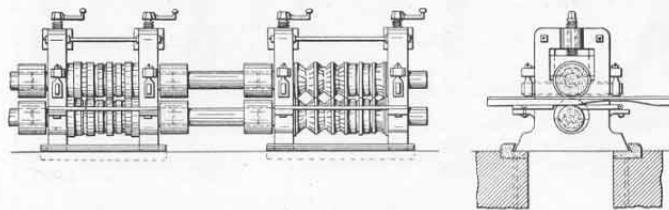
Walzwerk für Fischbauchschienen. Um 1823.
